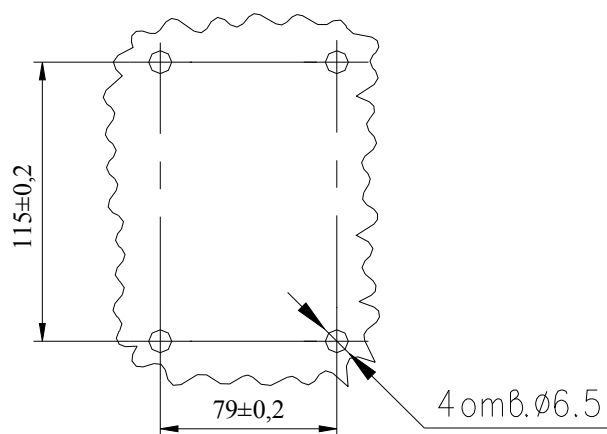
Устройство У4К, У4КМ, У2КМ. Габаритный чертеж
